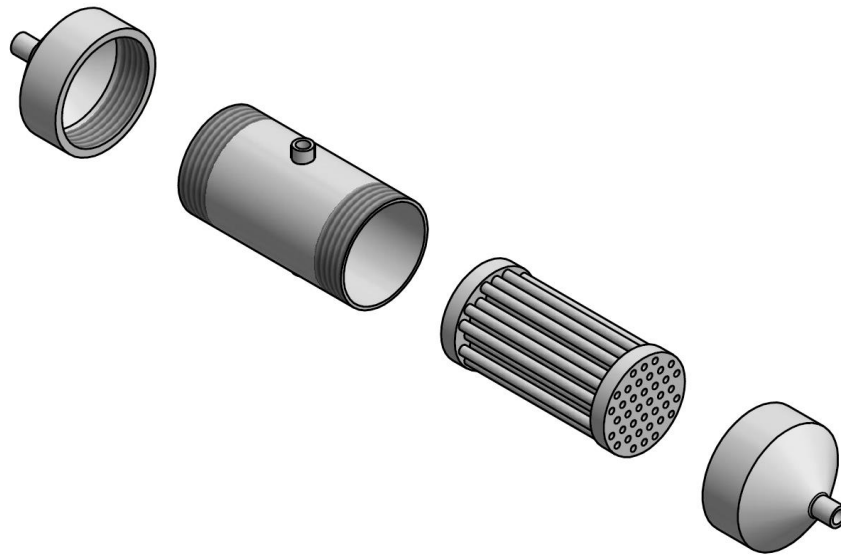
Explosión en 3D del oxigenador de membrana por impresión 3D
